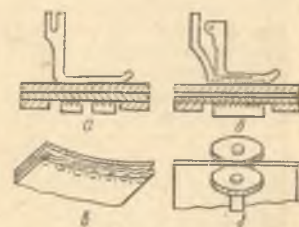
Продвигатели материалов с двумя рейками и рифлеными роликами
